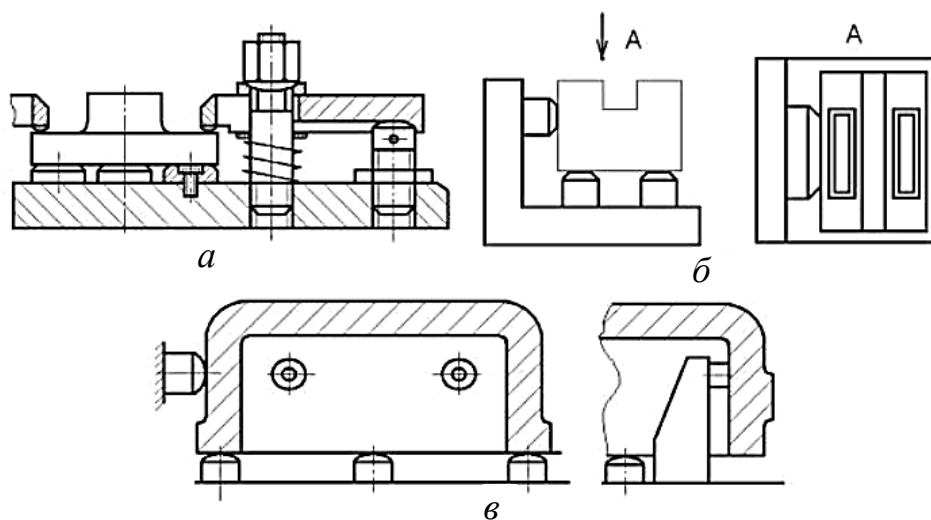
Схемы установки заготовок плоскими поверхностями на:
